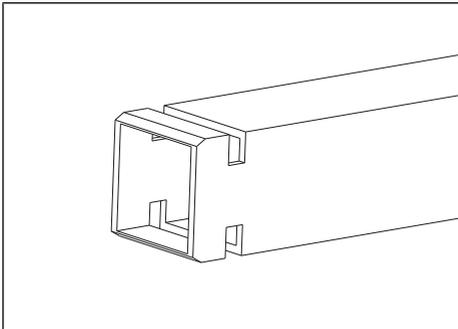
Évidements dans la poutre transversale Multi Wall
